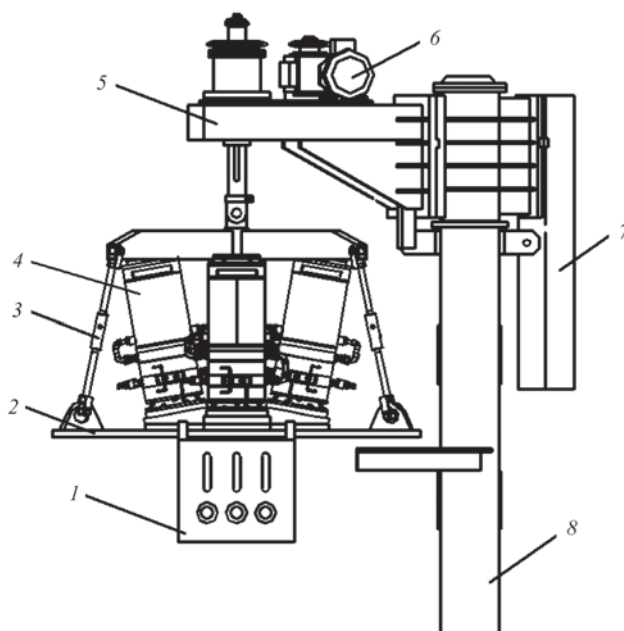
Устройство подъема и поворота с плитой ЭЛН: 1 — блок подачи рабочей газовой смеси; 2 — плита ЭЛН; 3 — регулируемая тяга; 4 — газоразрядная электронно-лучевая пушка; 5 — траверса; 6 — механизм подъема; 7 — противовес; 8 — колонна
